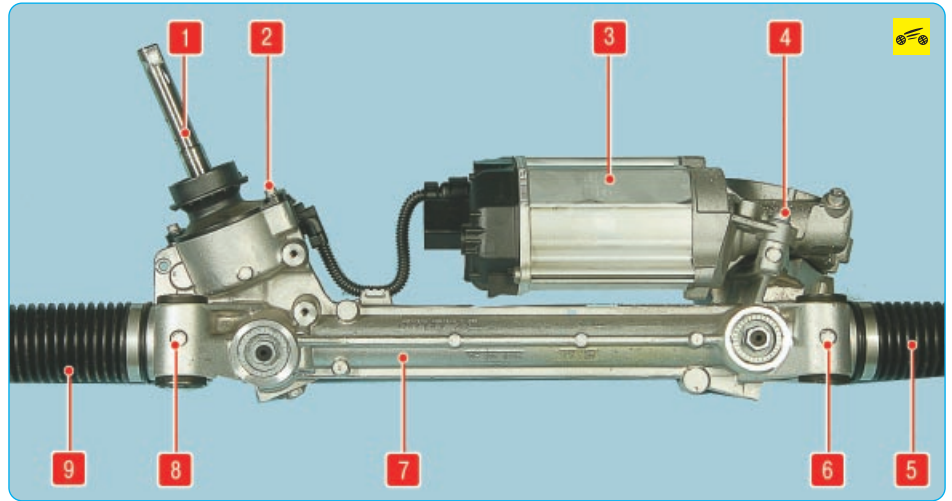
Рулевой механизм: 1 – вал-шестерня рулевого механизма; 2 – датчик положения рулевого вала; 3 – электродвигатель усилителя; 4 – редуктор усилителя; 5, 9 – защитные чехлы рулевых тяг; 6 – правая опора механизма; 7 – картер рулевого механизма; 8 – левая опора механизма
